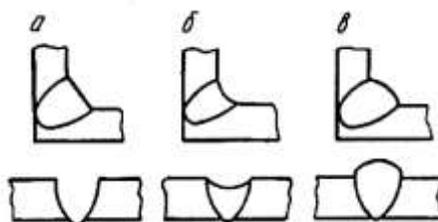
Виды сварных швов по типу усиления: а – нормальный; б – ослабленный; в – усиленный
